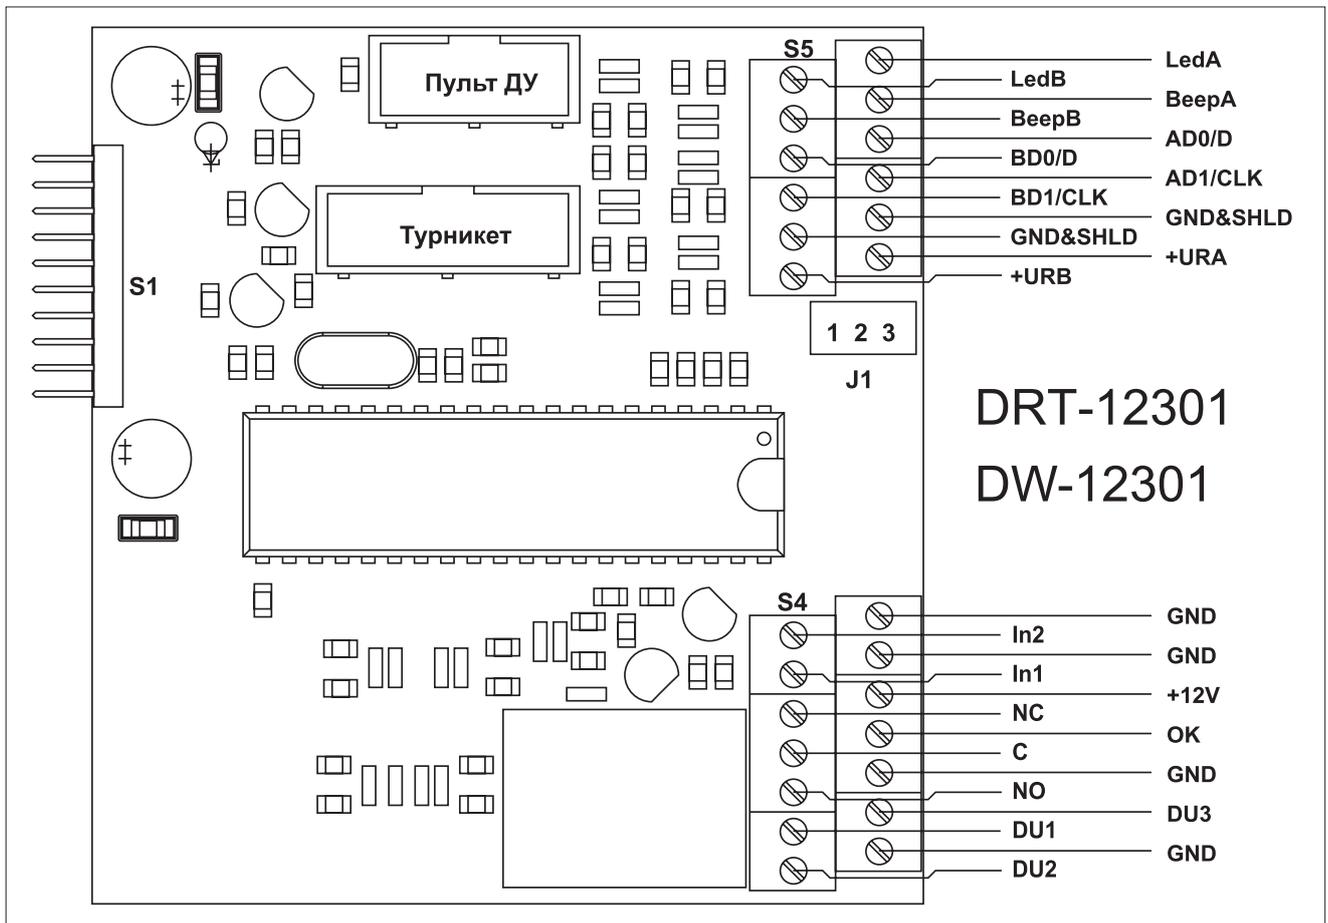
Внешний вид печатной платы DRT-12301 в сборе
